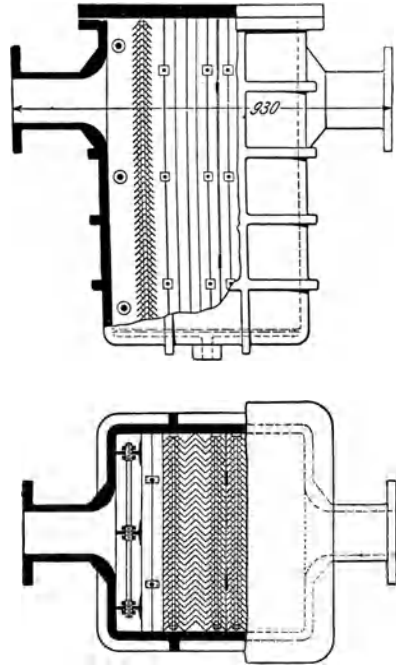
und 126. Stoßkraftentöler zur Entölung des Abdampfes von Kolbenmaschinen.
